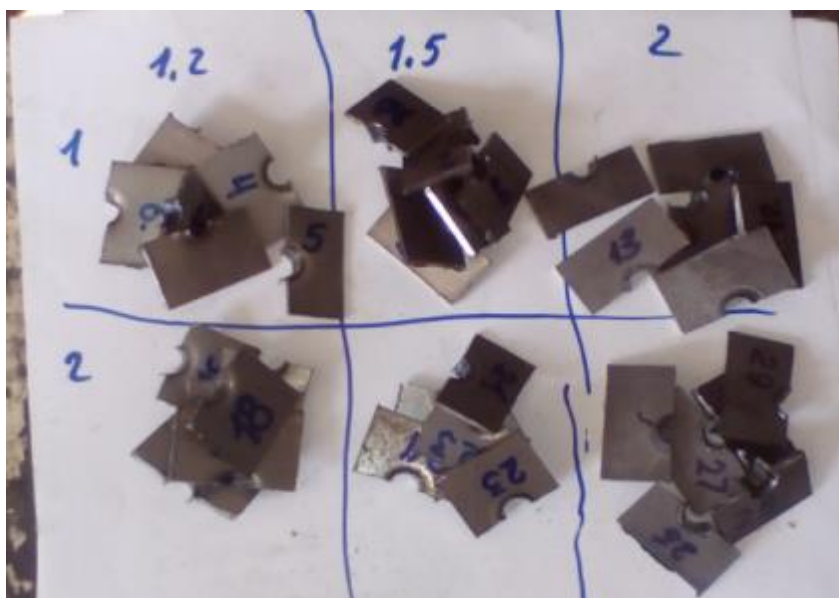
Распиленные заготовки для дальнейшего измерения геометрических параметров
